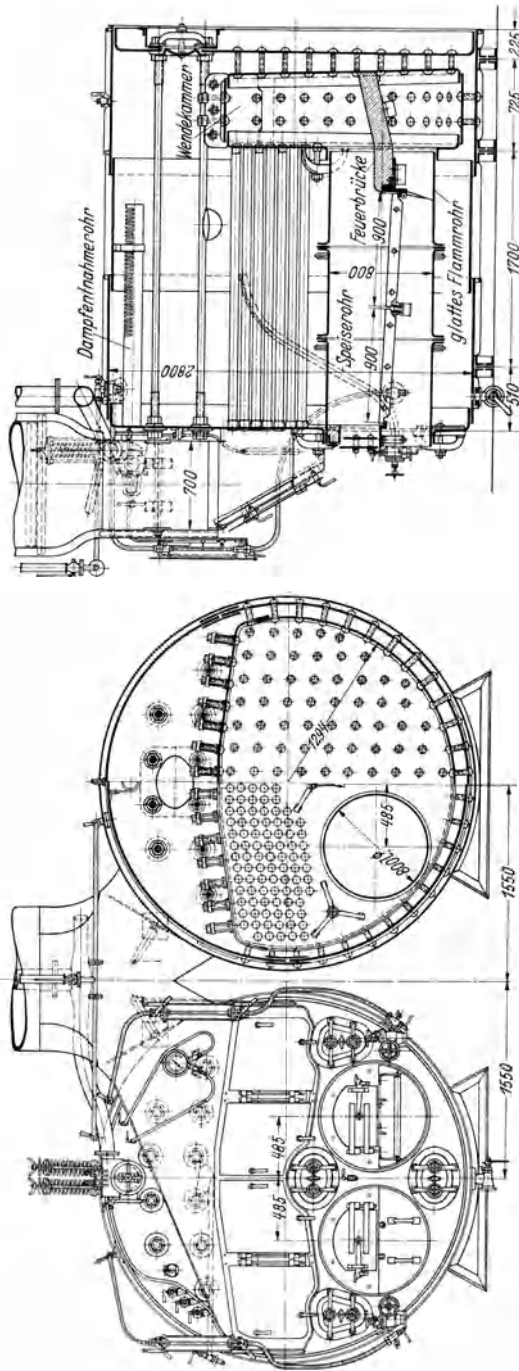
Einender-Schiffskessel. Man beachte das glatte Flammrohr, die für beide Flammrohre dienende einteilige Wendekammer mit ihrer starken Stehbolzenverankerung und das auf der Oberseite mit Eintrittsschlitten versehene Dampfnahmerohr.
